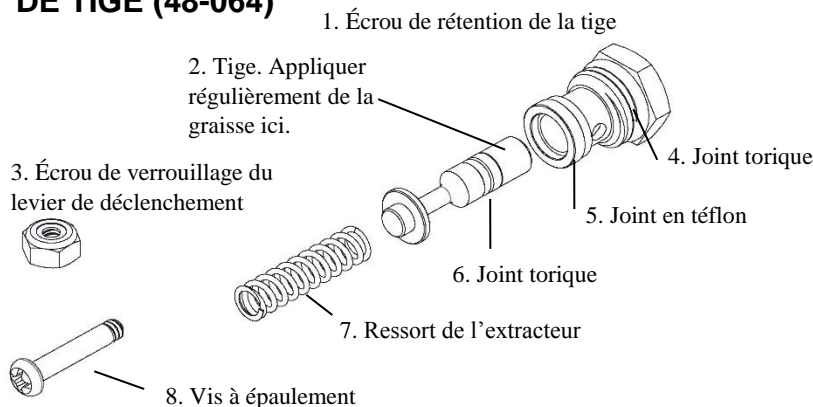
Figure E : ENSEMBLE DE REMPLACEMENT DE TIGE (48-064)
